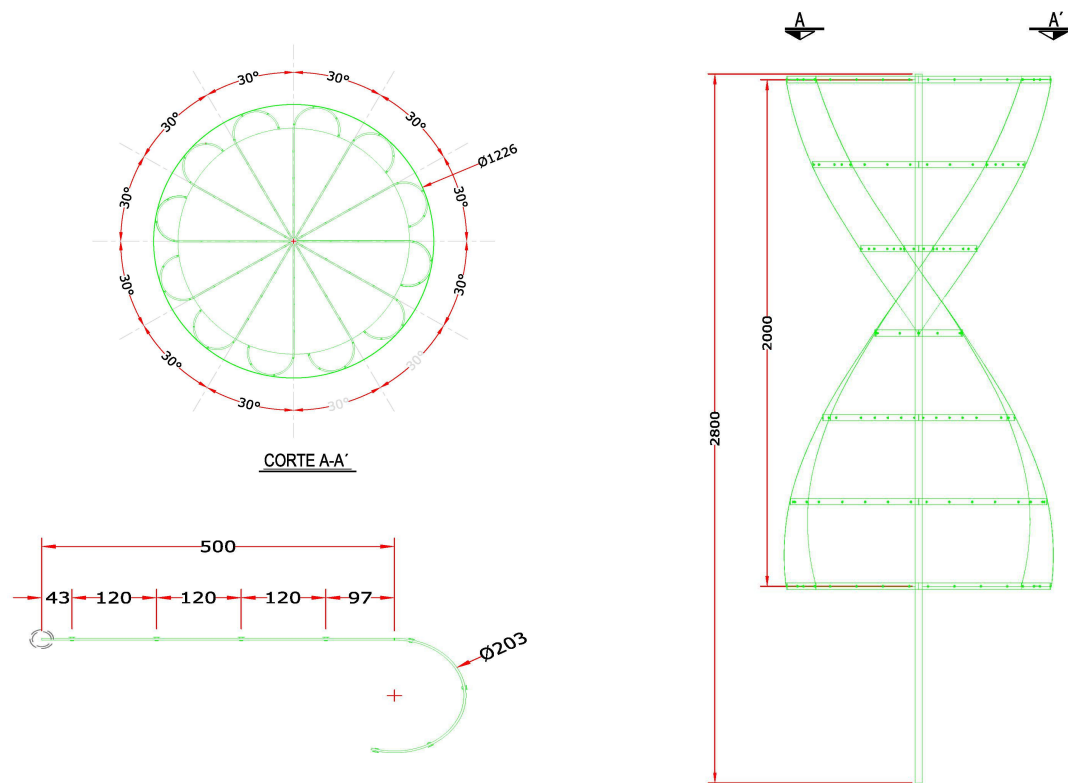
Dimensiones de prototipo HelixWind, Dimensiones en mm.
